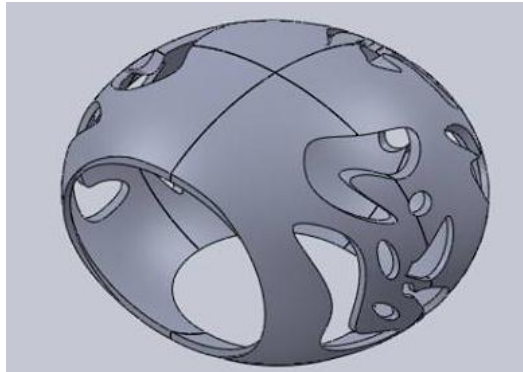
Cabeza del Robot diseñada en SolidWorks
